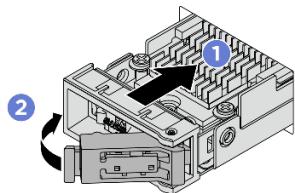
Installieren einer M.2-Laufwerkbaugruppe
